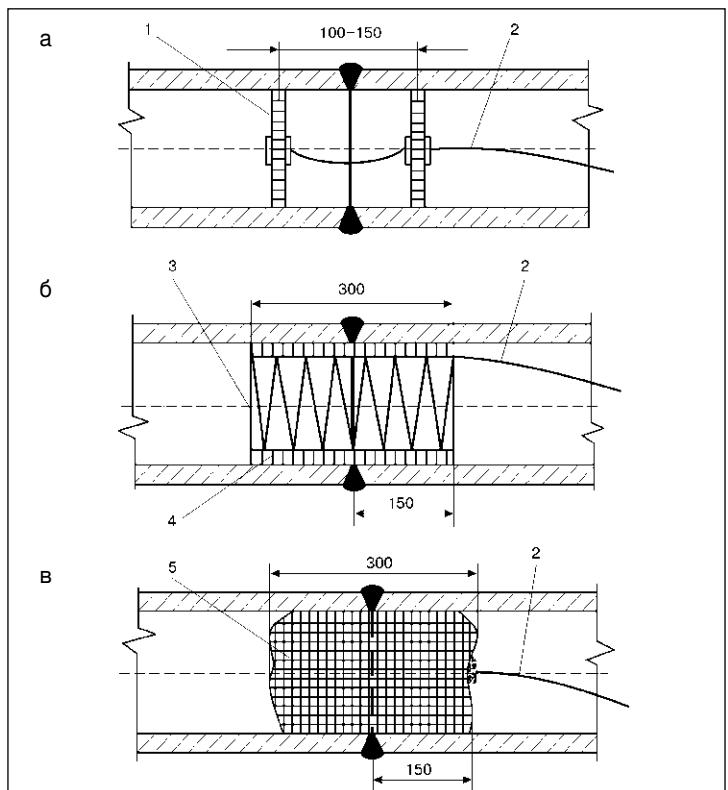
Способы установки теплоизоляции в полость сварных соединений трубопроводов: а — установка заглушек; б — установка подкладок; в — установка теплоизоляционного мешка (1 — заглушки; 2 — проволока для удаления теплоизоляционного устройства; 3 — проволочный прижим; 4 — подкладка из ткани КТ-11 или асбестовой ткани; 5 — теплоизоляционный мешок из ткани КТ-11 или асбестовой ткани с набивкой из рулонного материала ВКР-150)
